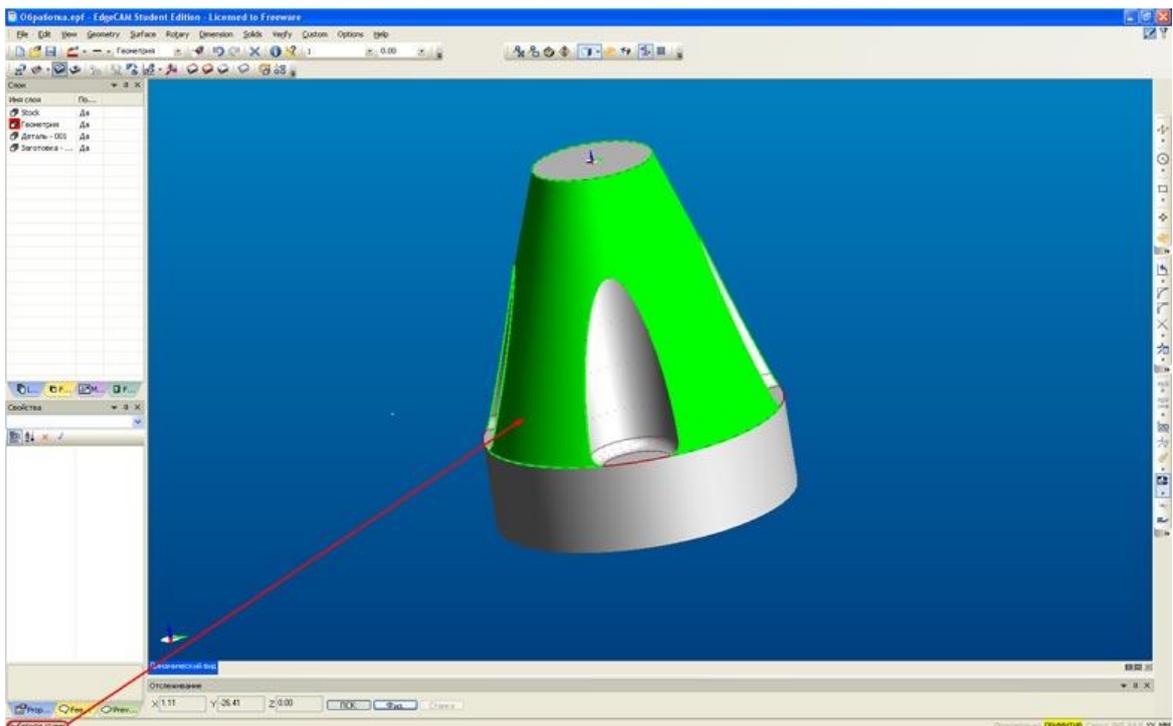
Edgescam. Выбрать обрабатываемые поверхности
